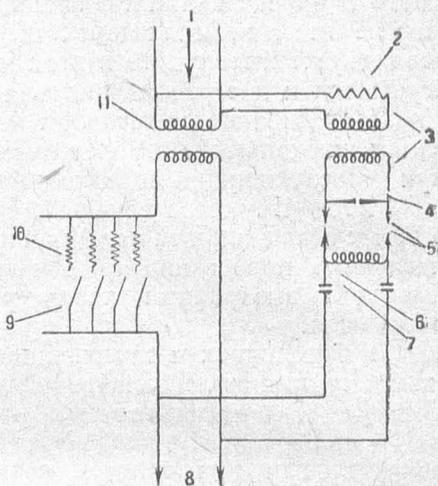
Схема осциллятора. 7 — сеть; 2 — резистор; 3 — трансформатор напряжения; 4 — конденсатор; 5 — искровой разрядник; 6 — индукционная катушка; 7 — конденсатор; 8 — сварочная цепь; 9 — рубильники; 10 — регулировочный резистор; 11 — сварочный трансформатор
